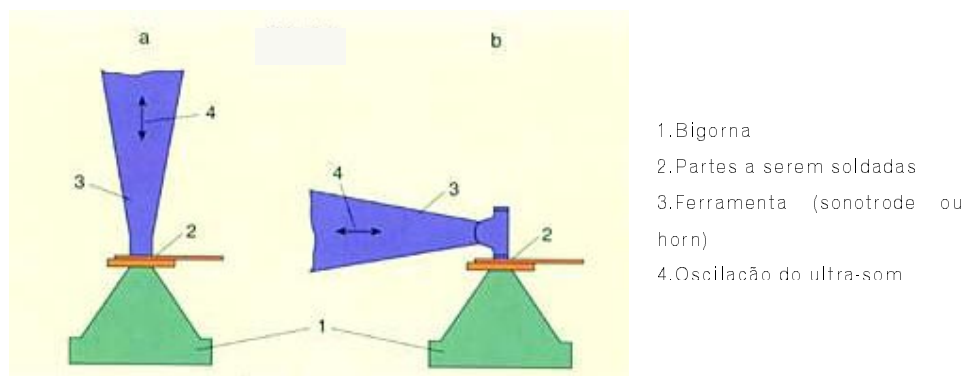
Diferenças do processo de soldagem por ultra-som de plásticos e metais.
